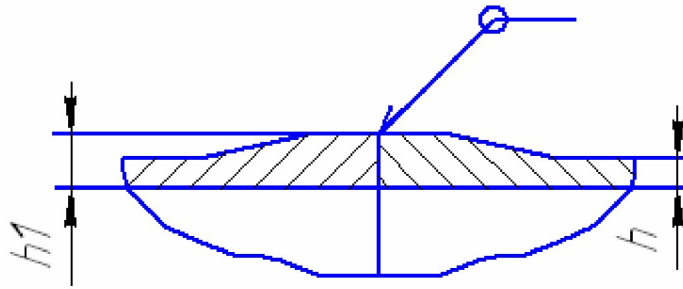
Стыковое сварное соединение с усилением кромок
